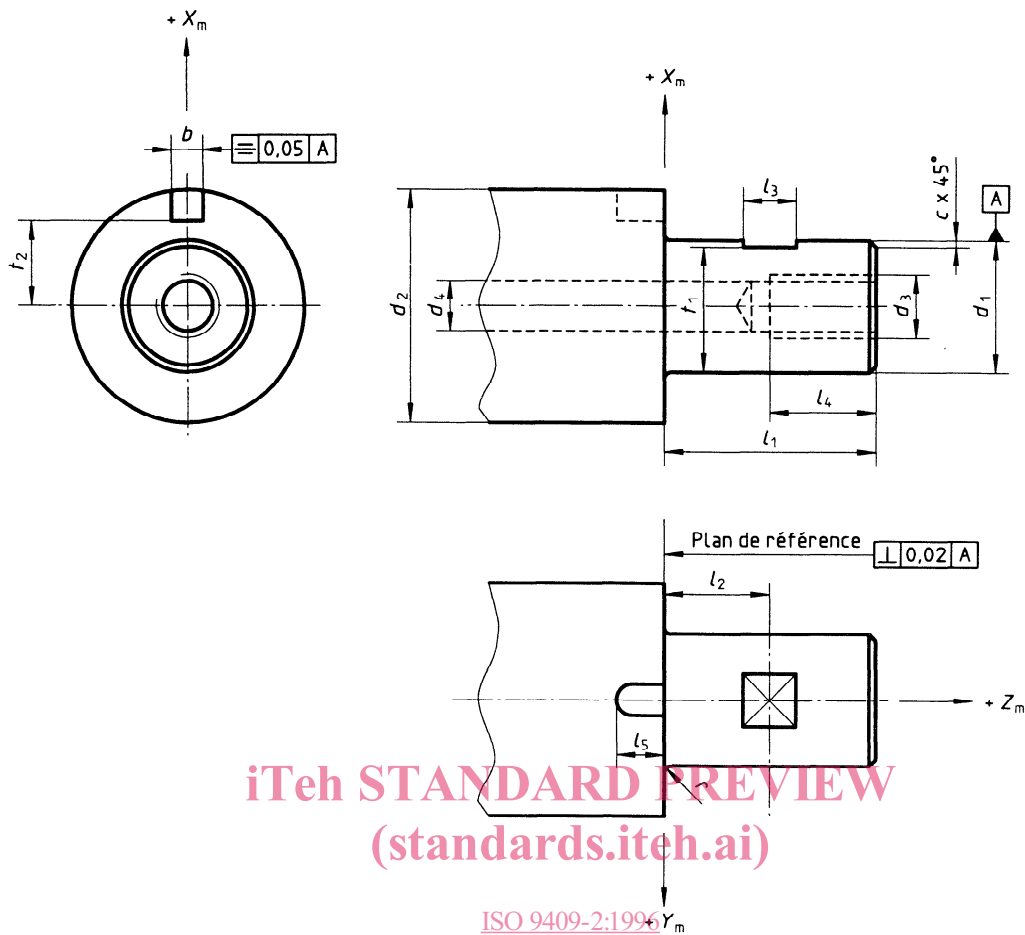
Dimensions de base des interfaces mécaniques à queue de type 1
